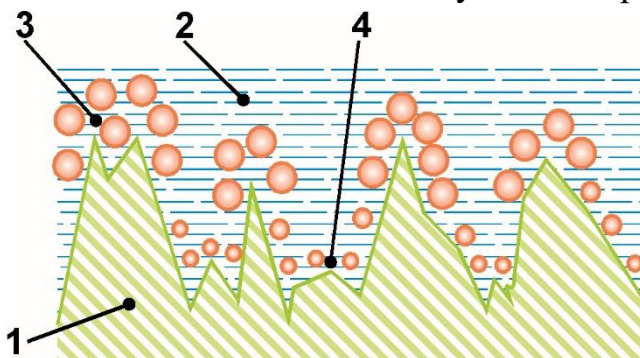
Схема процесу хімічної обробки, де основний метал (1); плівка (2); місця активного знімання матеріалу (3); місця уповільнених реакцій (4)
